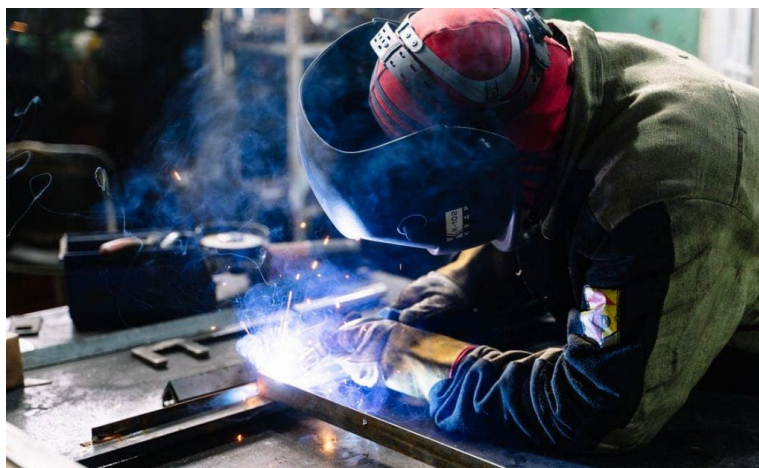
Ремонтная сварка самозащитной проволокой
